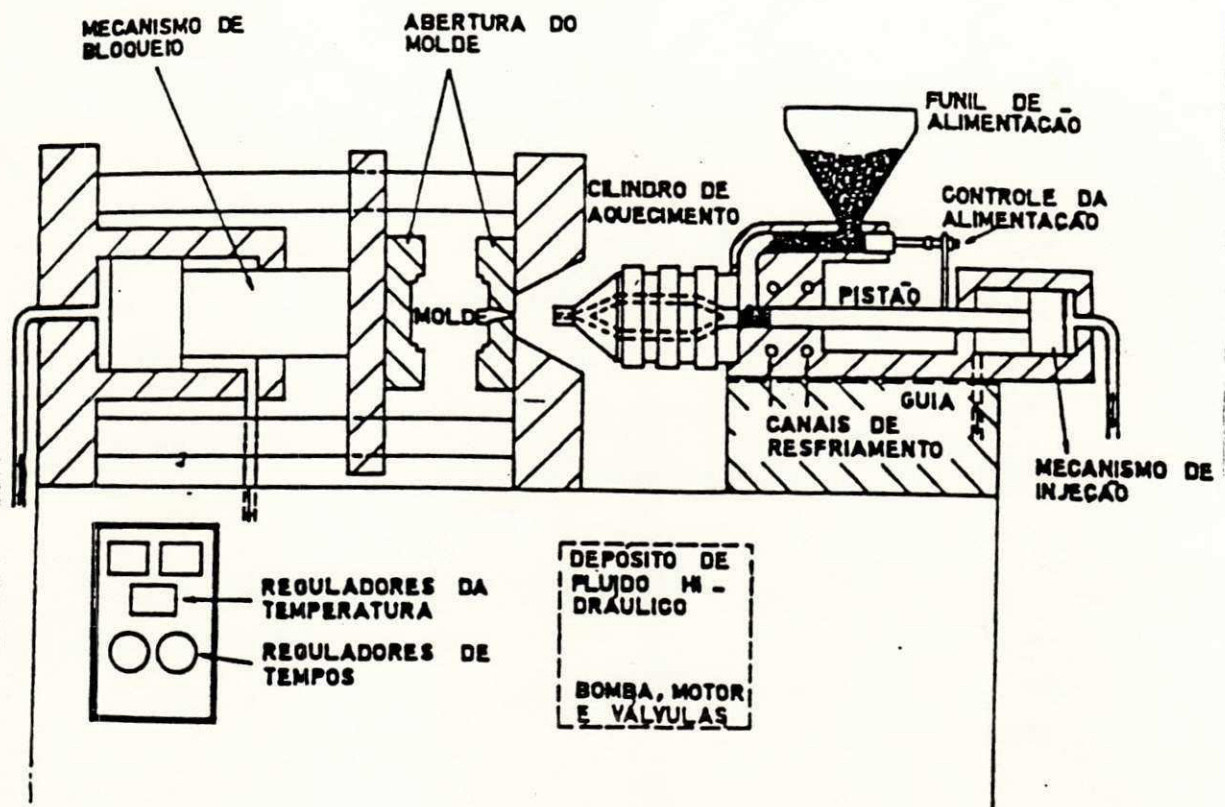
Máquina de Moldagem por Injeção Tipo Pistão
